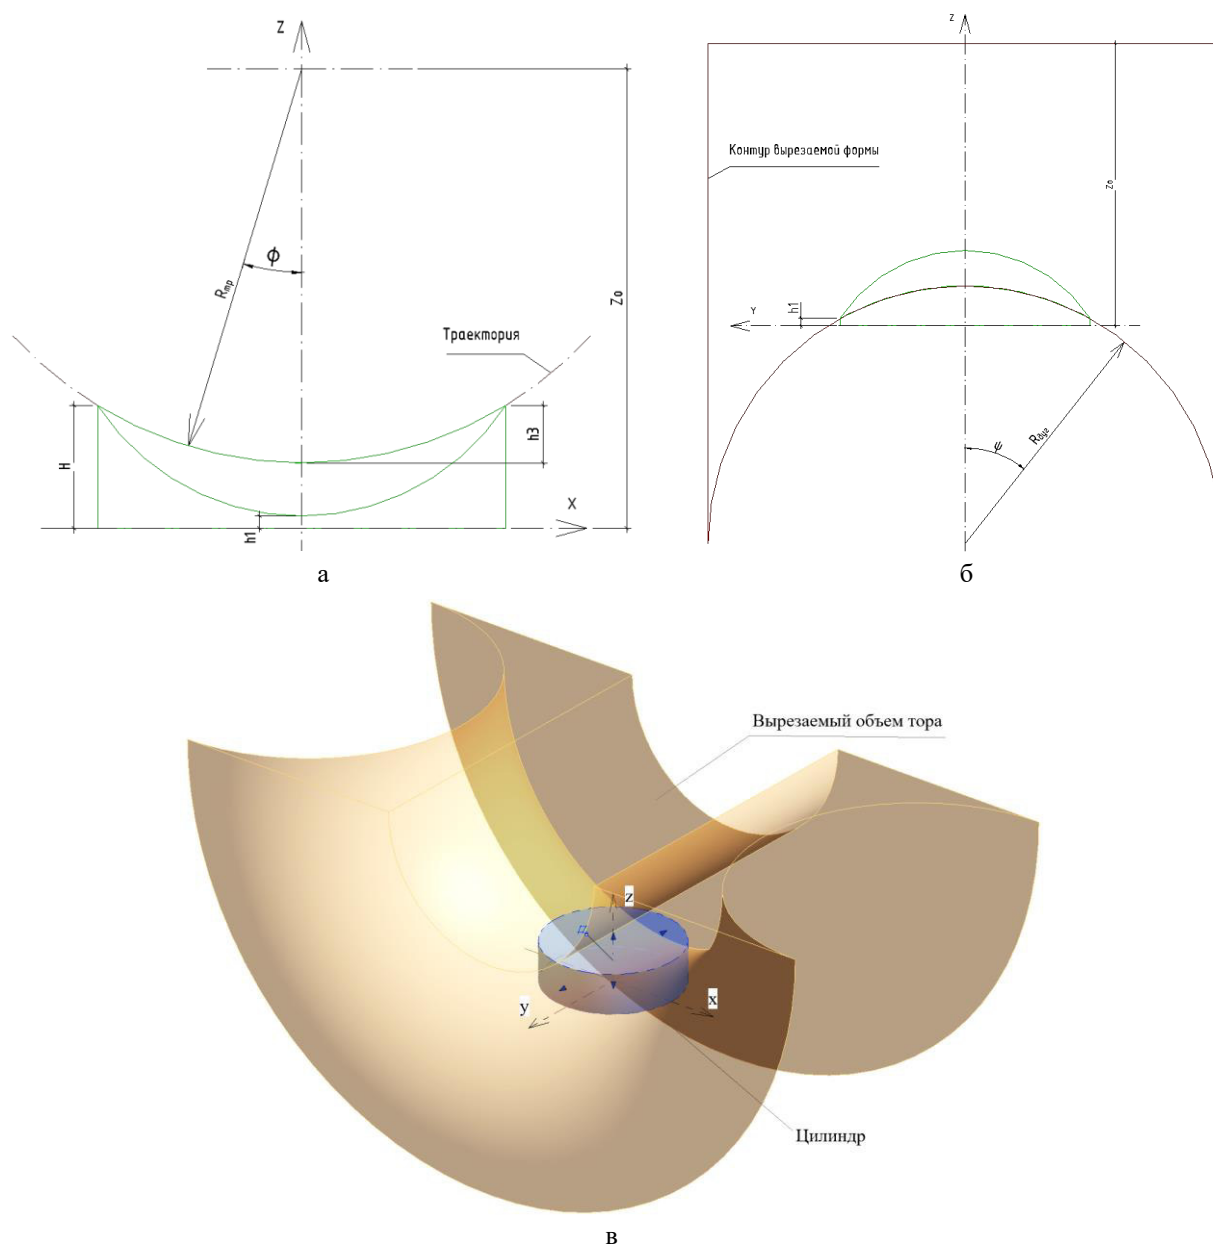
Геометрическая схема тороидной поверхности: а – вид спереди; б – вид сбоку; в – общий вид
